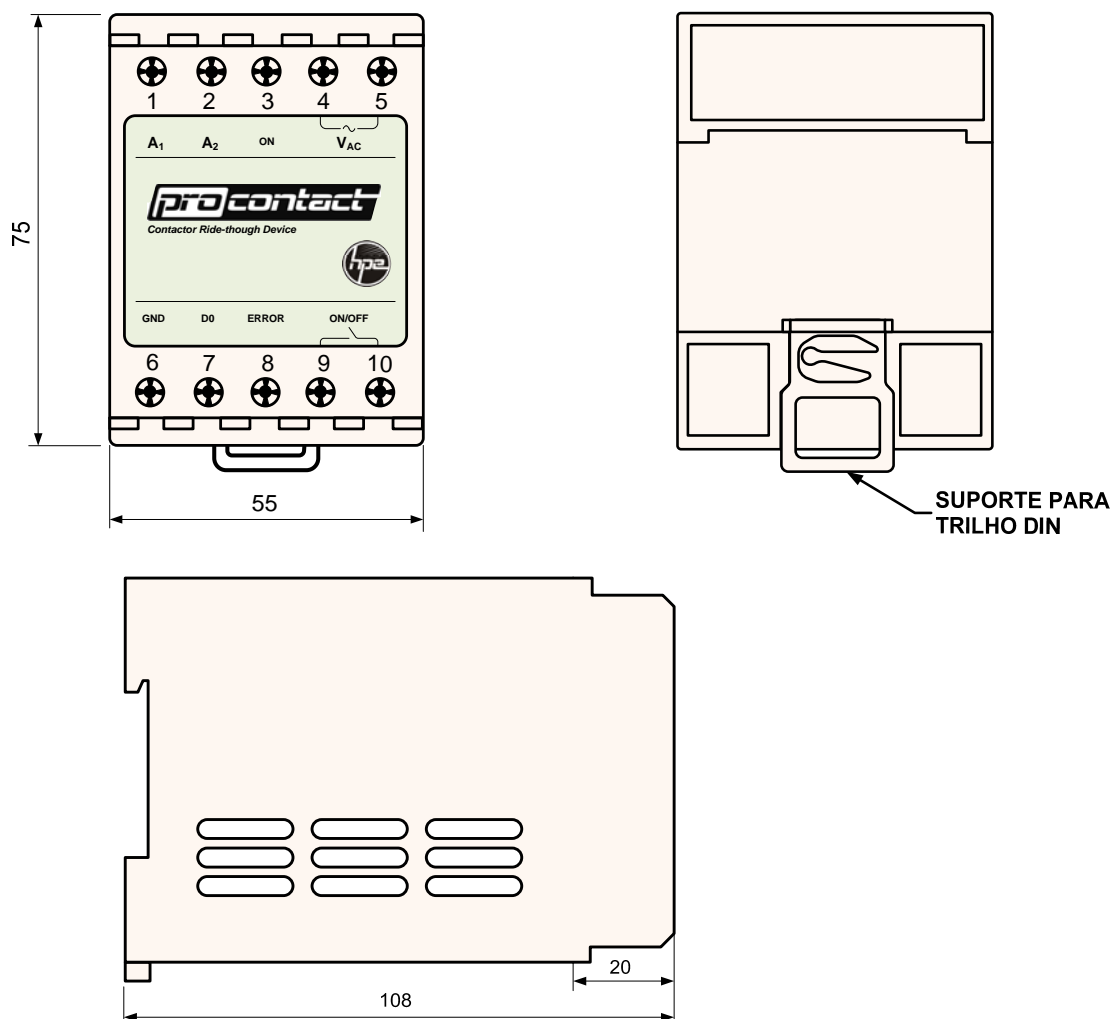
Esquemático dimensional do PRO CONTACT[®].
